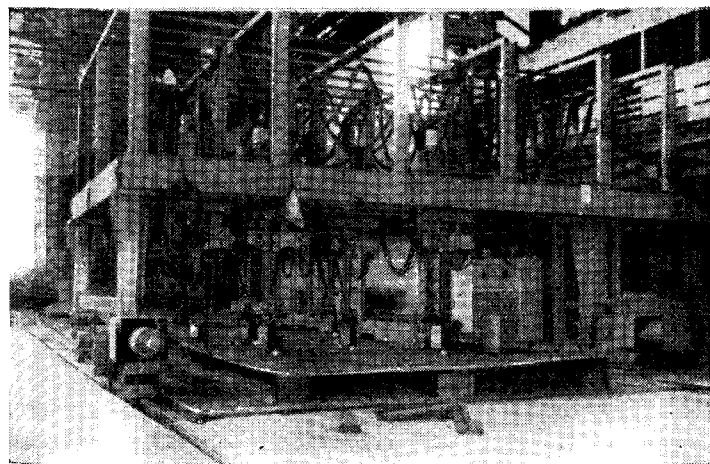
Автоматический гибочный пресс для листового материала с использованием подогрева газовыми горелками. Прессы употребляют для гибки листов больших размеров, формирующих носовую и кормовую части судна. Движение каждой газовой горелки контролируется самостоятельным фотоэлектрическим элементом.
